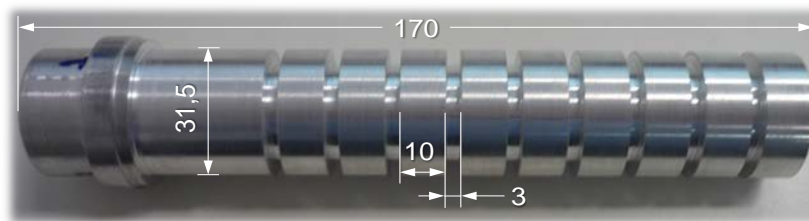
Geometria do corpo de prova antes da usinagem.
